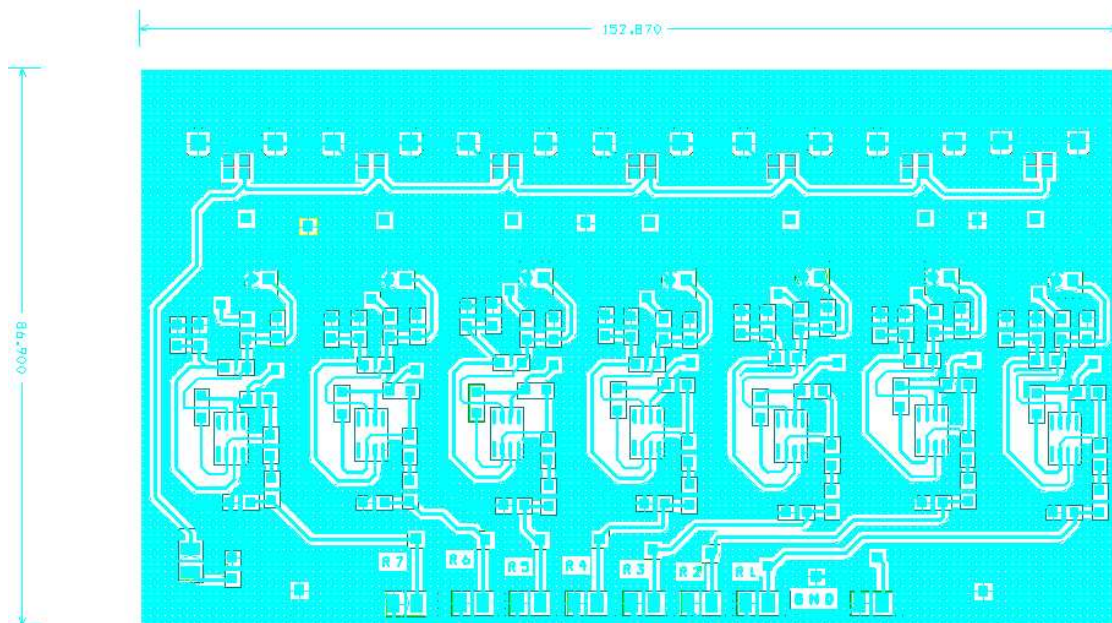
Layout do PCB da placa de apoio à *LocusBoard* - Top.
